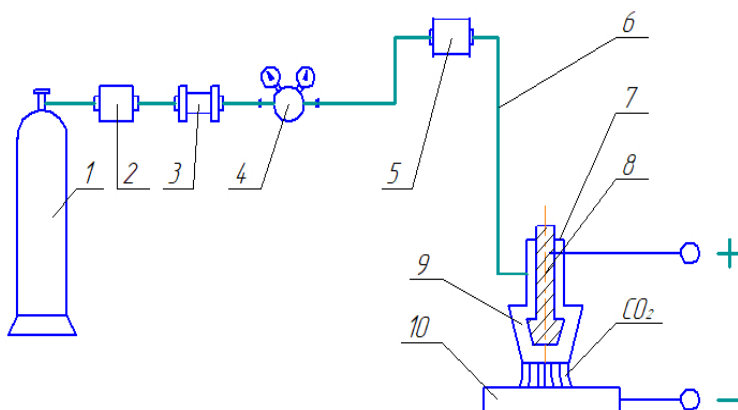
Схема индивидуальной системы газопитания при дуговой сварке в углекислом газе: 1 — баллон с  $CO_2$ ; 2 — подогреватель  $CO_2$ ; 3 — осушитель  $CO_2$ ; 4 — газовый редуктор–расходомер У-30; 5 — электромагнитный клапан; 6 — шланг; 7 — сварочная горелка; 8 — токоподводящий мундштук; 9 — сопло горелки; 10 — изделие
